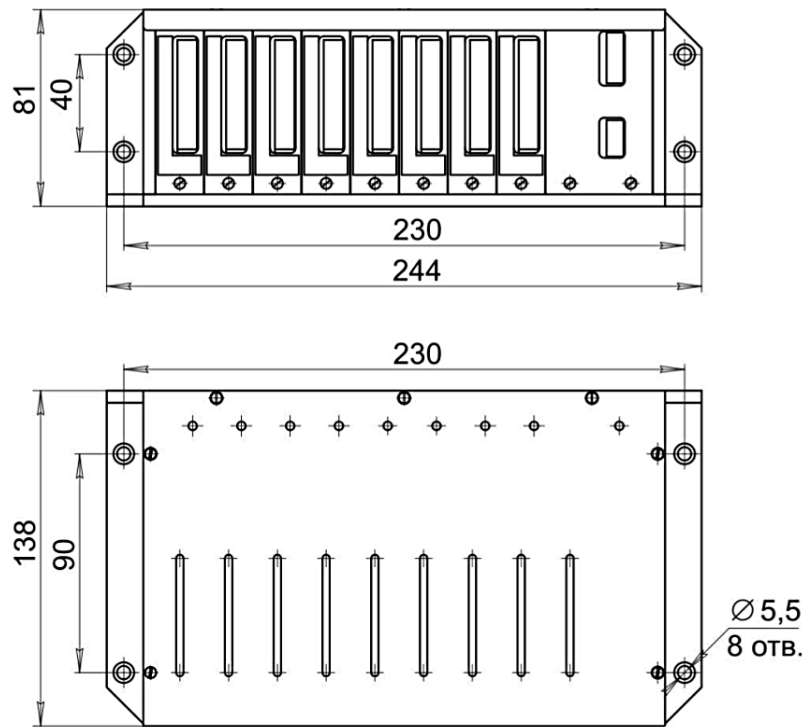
Габаритные и установочные размеры блока модулей БМ-8
